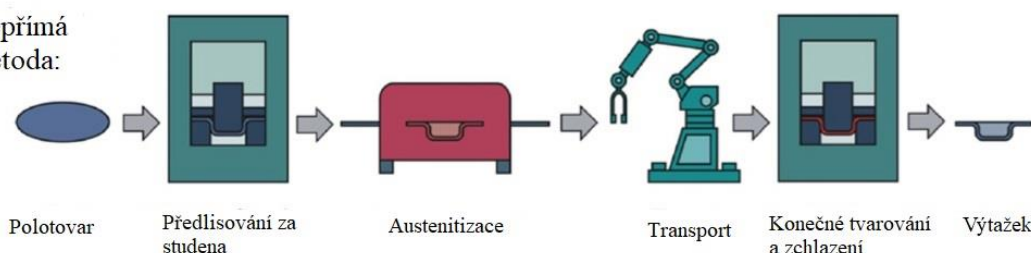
Schéma přímé metody „hot stamping“ [10]
